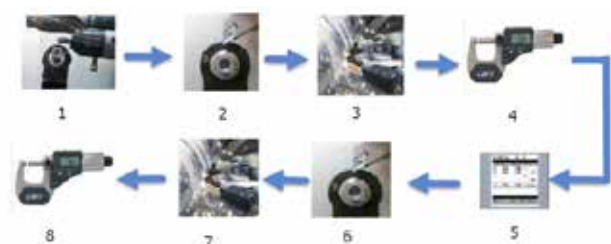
Schemat planu badawczego dla przyjętych procedur
